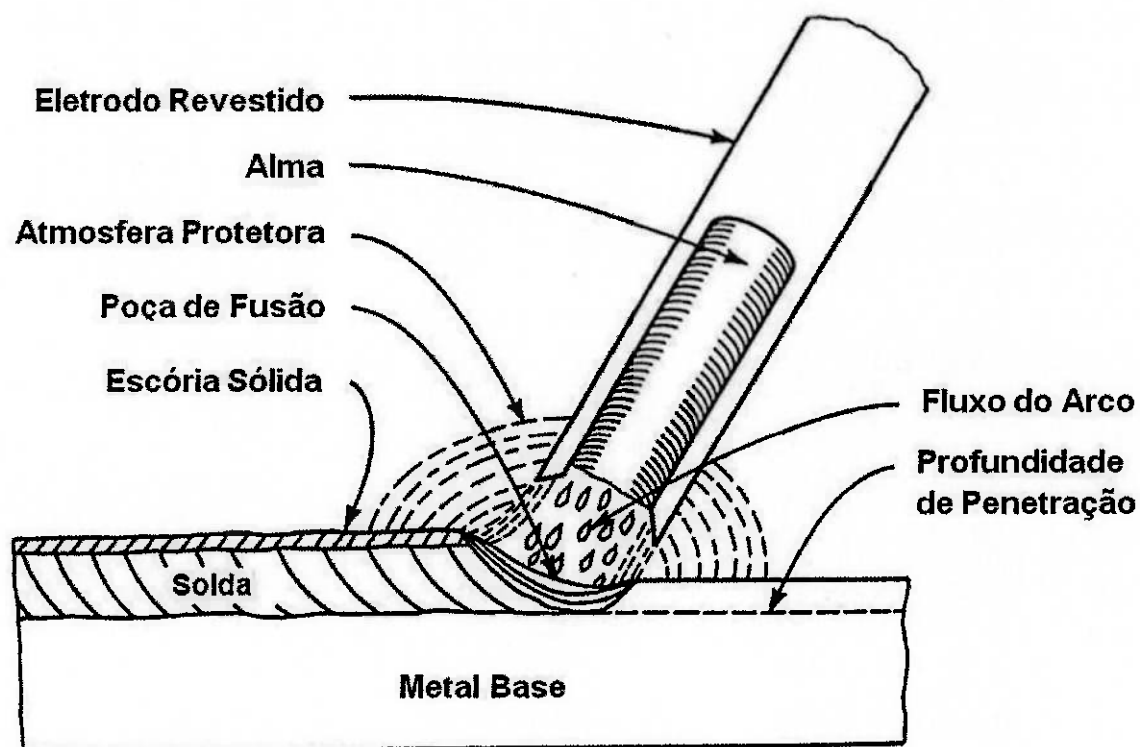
Esquema do Processo de Soldagem por Eletrodo Revestido [5].
